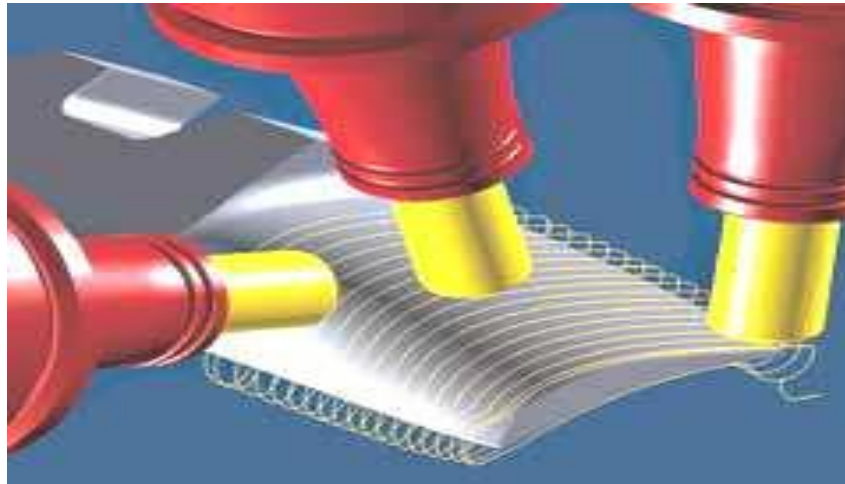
Usinage en bout d'aube de turbine 5 axes [8]
